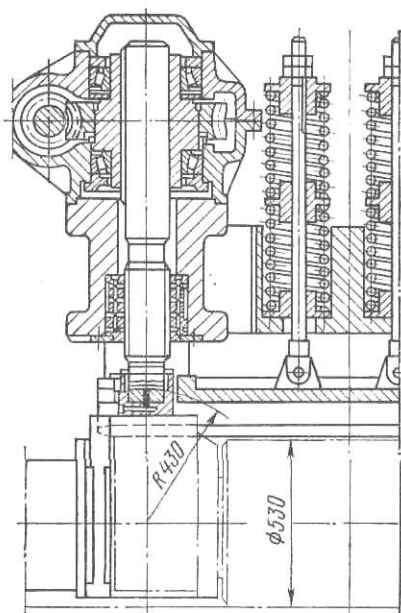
Пружинное уравнивание верхнего валка клетки 530 мм непрерывного заготовочного стана 700/500
